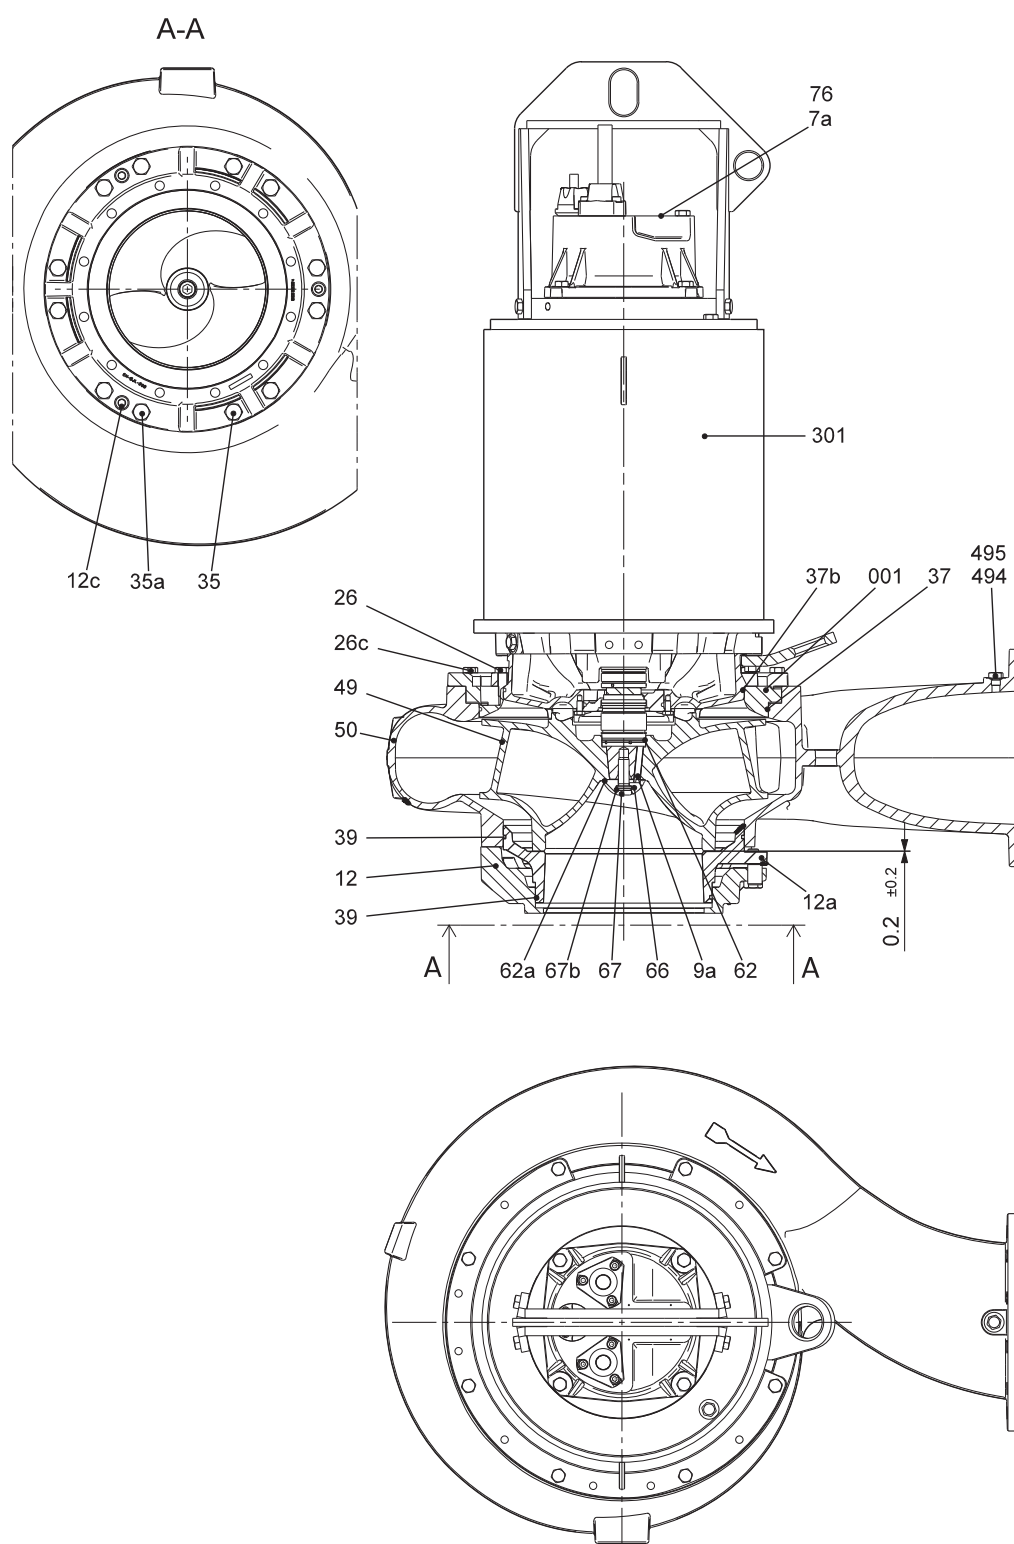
Взрывозащищённый двигатель с охлаждающим кожухом
